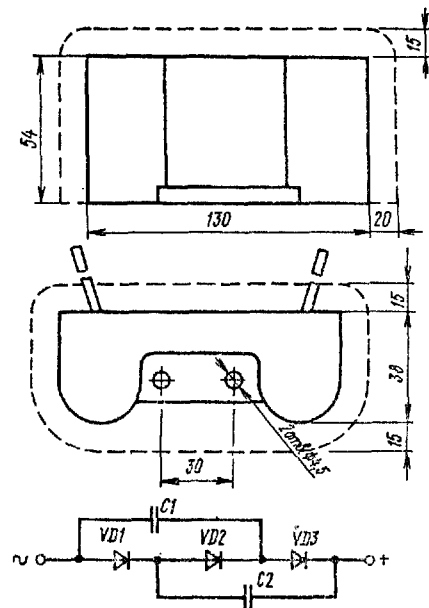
Общий вид, габаритные, присоединительные размеры и электрическая схема умножителя УН9/18-0,3
